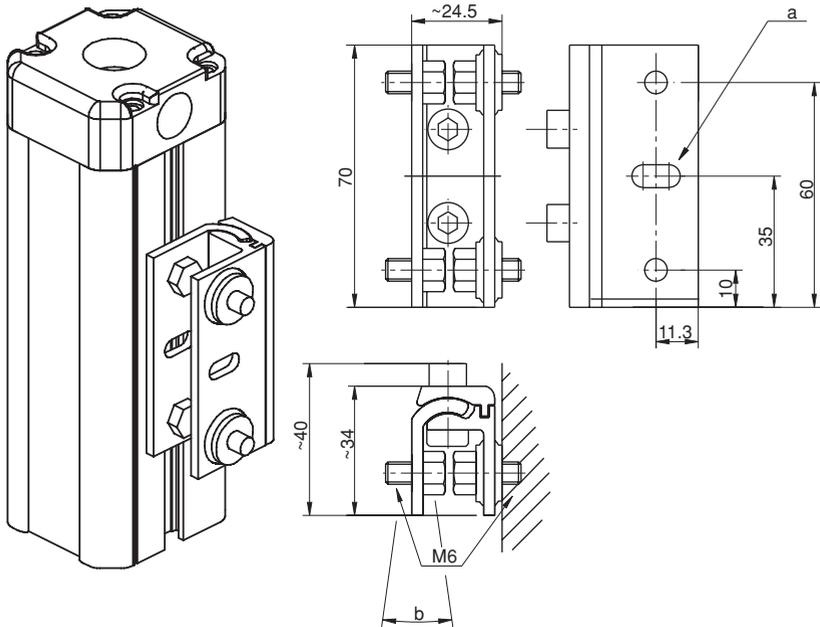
Schwenkbare Halterung mit Schwingungsdämpfung
